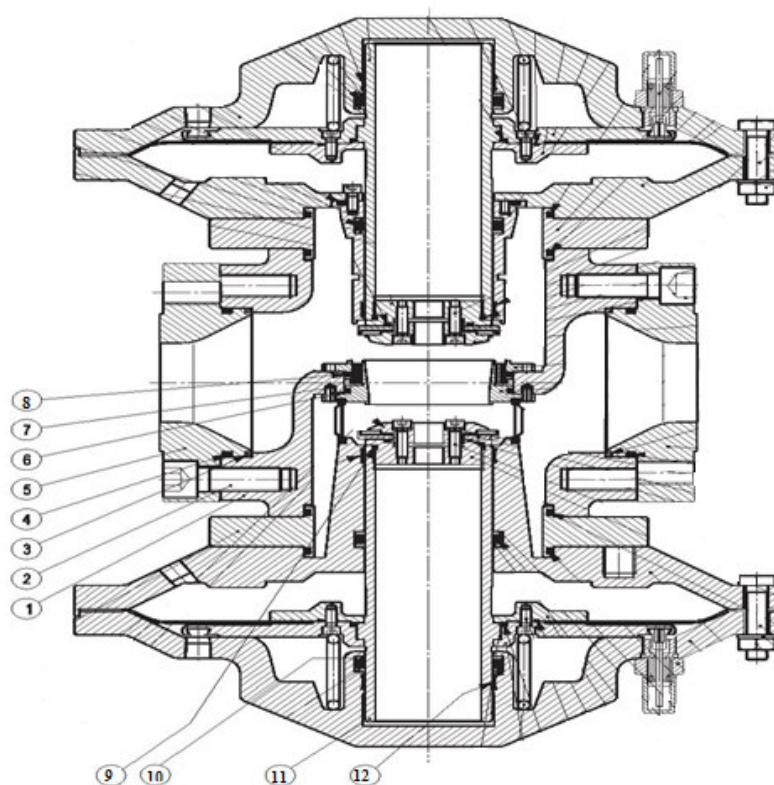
Схема регулятора давления: 1 - корпус, 2 - винт, 3- металлическая прокладка, 4 - пластина, 5- фланец входа/выхода, 6 - уплотнительное кольцо, 7- эластичный фиксатор, 8- прокладка предохранительно-запорного клапана, 9 - уплотнительное кольцо, 10 - антифрикционное кольцо, 11- затвор, 12- фиксатор прокладки
